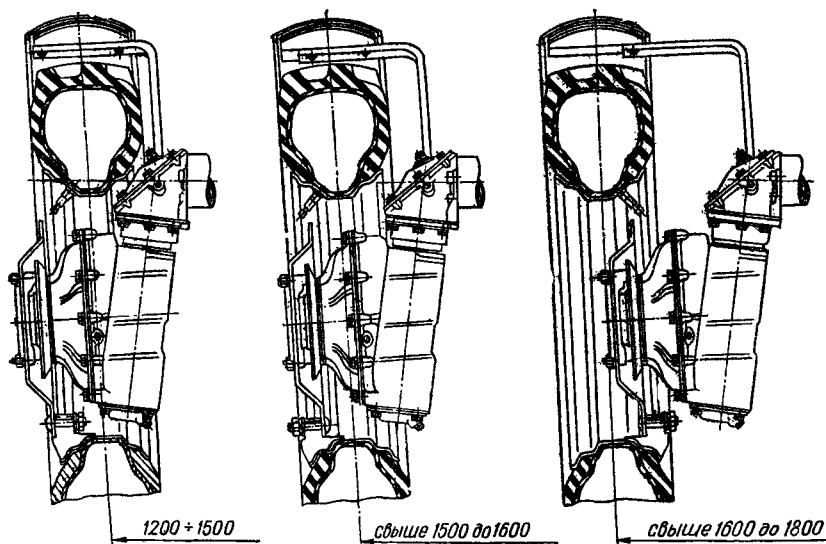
Схема установки передних колес тракторов МТЗ-82 и МТЗ-82Л на различную колею.
